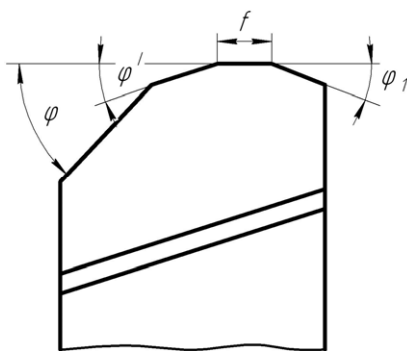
Схема резца В.А. Колесова для силового резания
